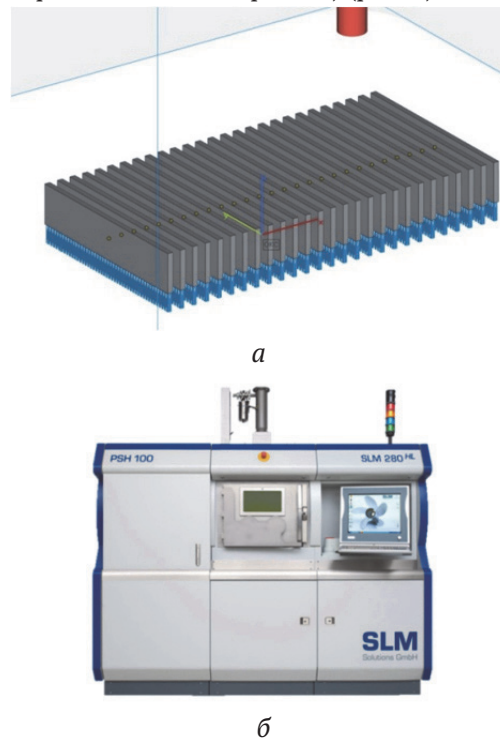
Образцы из жаропрочного сплава ВЖ-159 (ХН58МБЮ) (а) и установка селективного лазерного плавления SLM 280 HL (б)
